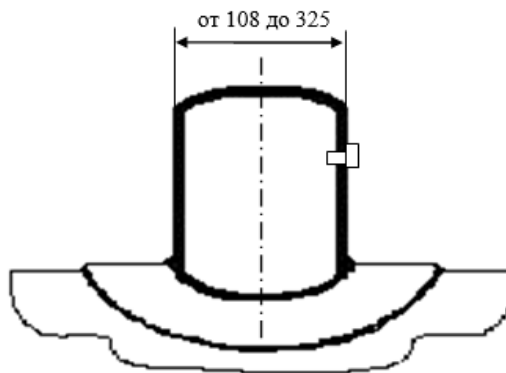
Патрубок с усиливающей накладкой типа П7 [3]
